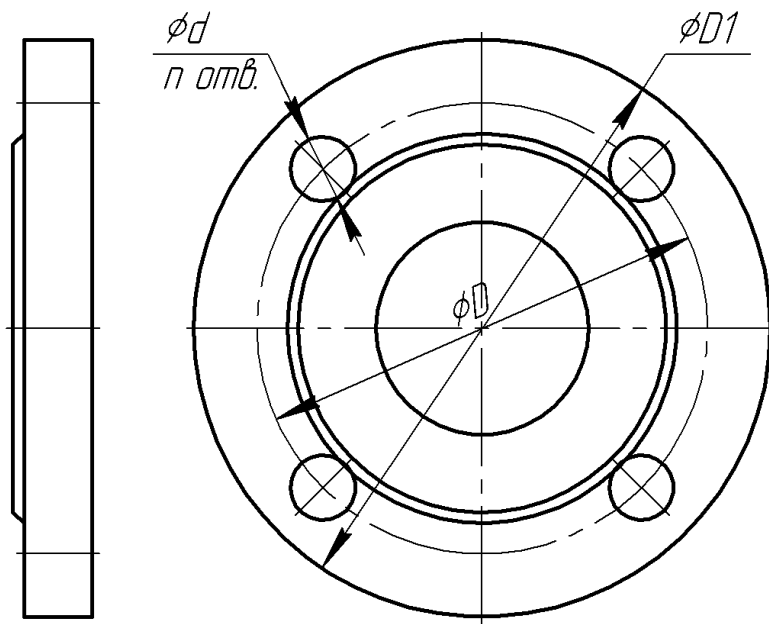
Габаритные и присоединительные размеры БМУ-08 (6 мм)
